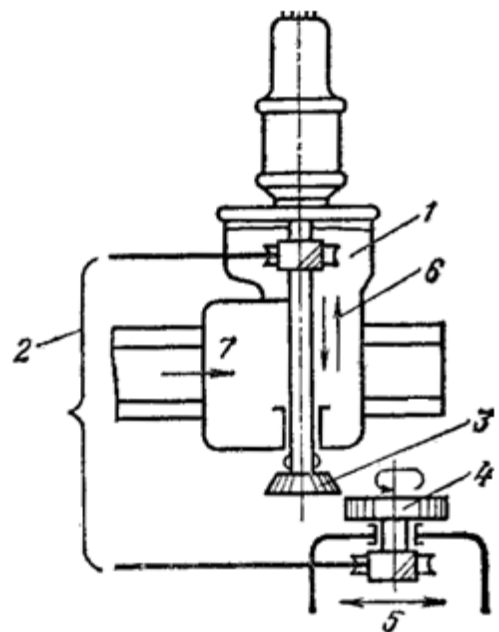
Движение рабочих органов зубодолбежного станка:
